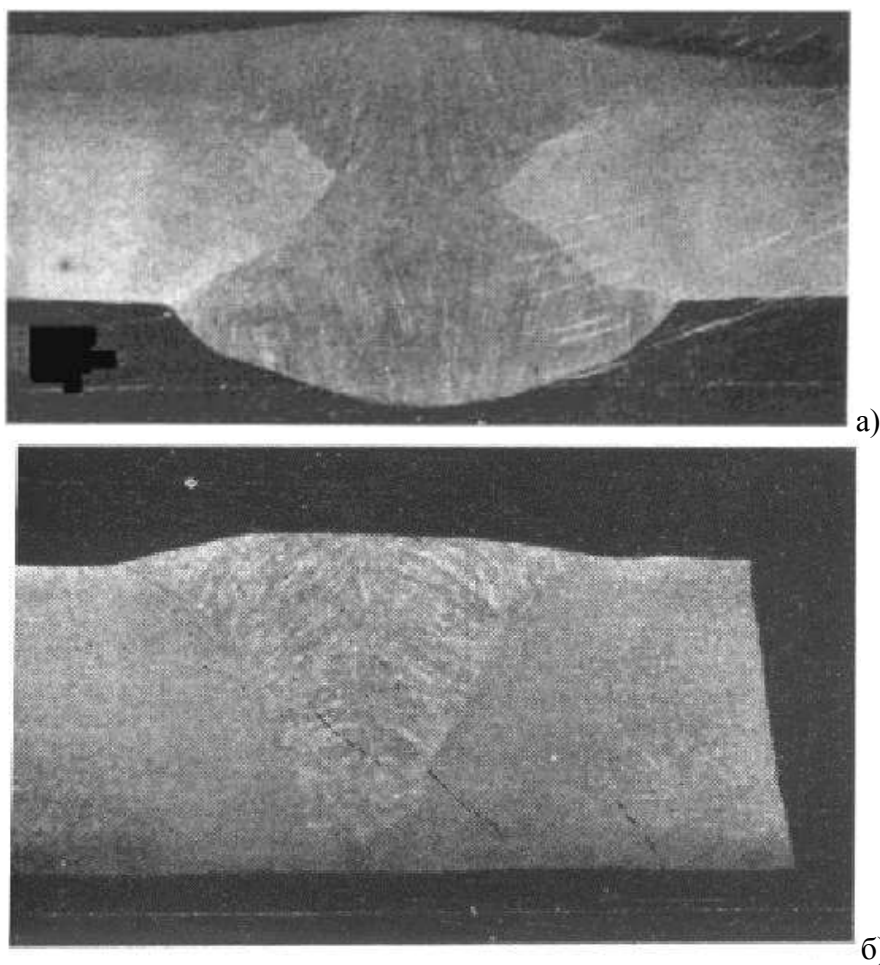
Макроструктура сварных швов: а) стыковой шов, односторонняя сварка; б) стыковой шов, двухсторонняя сварка x5
